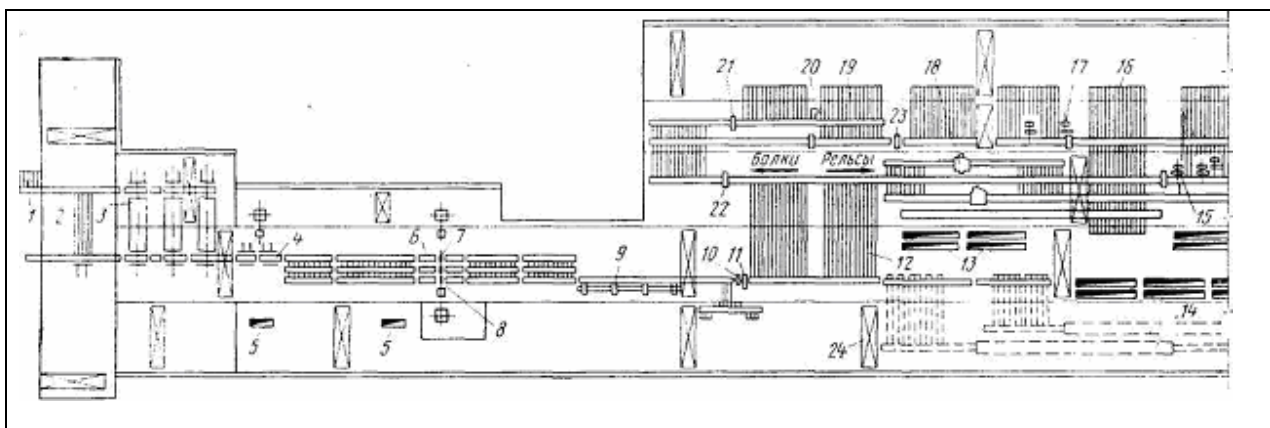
План расположения оборудования линейного рельсобалочного стана 950/800 конструкции УЗТМ:
